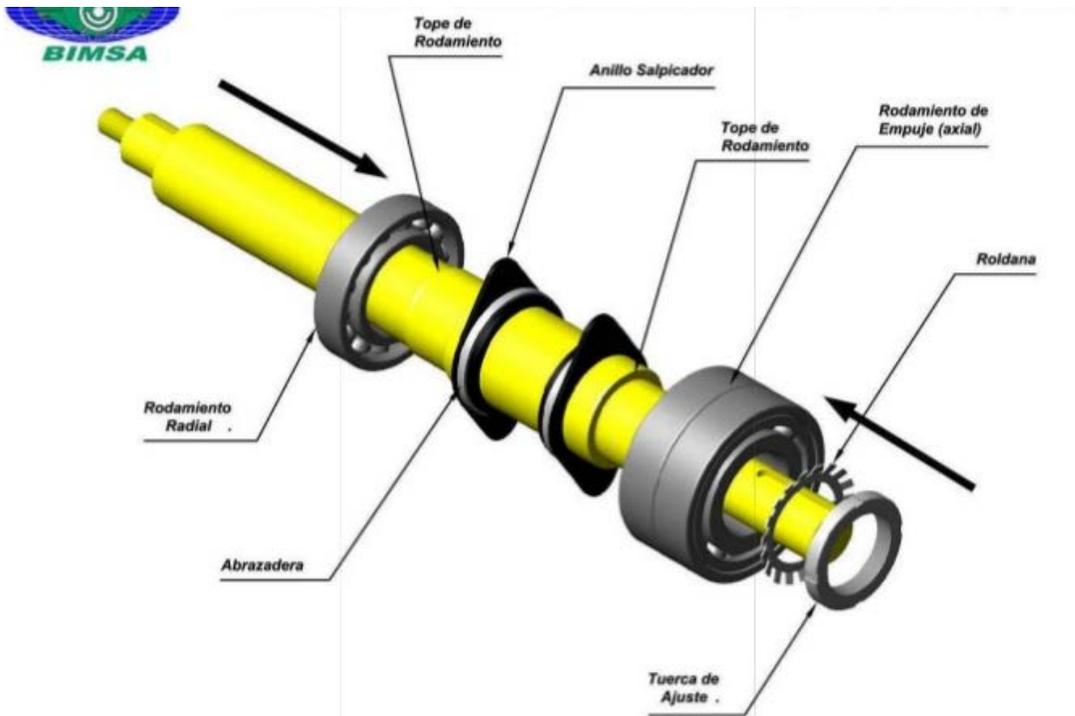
MONTAJE DE ANILLOS Y RODAMIENTOS
